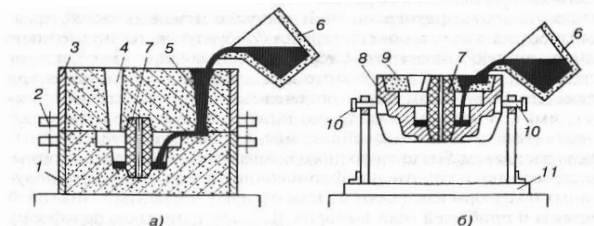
Литейные формы для разового (а) и многократного (б) использования: 1, 3 - нижняя и верхняя полуформы; 2, 10 - цапфы; 4 - выпор; 5 - расплав; 6 - ковш; 7, 9 - стержни; 8 - металлическая форма (кокиль); 11 - основание кокиля
